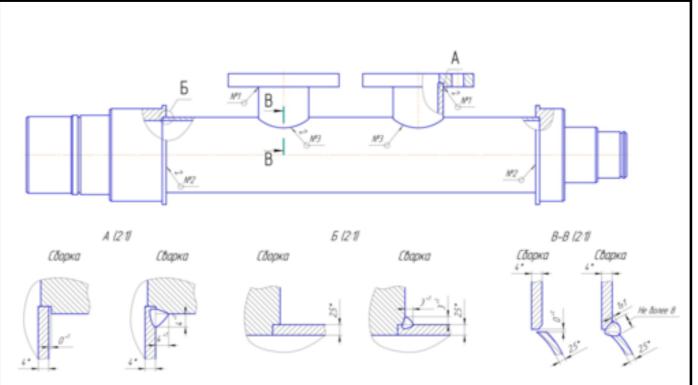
Схема расположения и общий вид сварных швов
